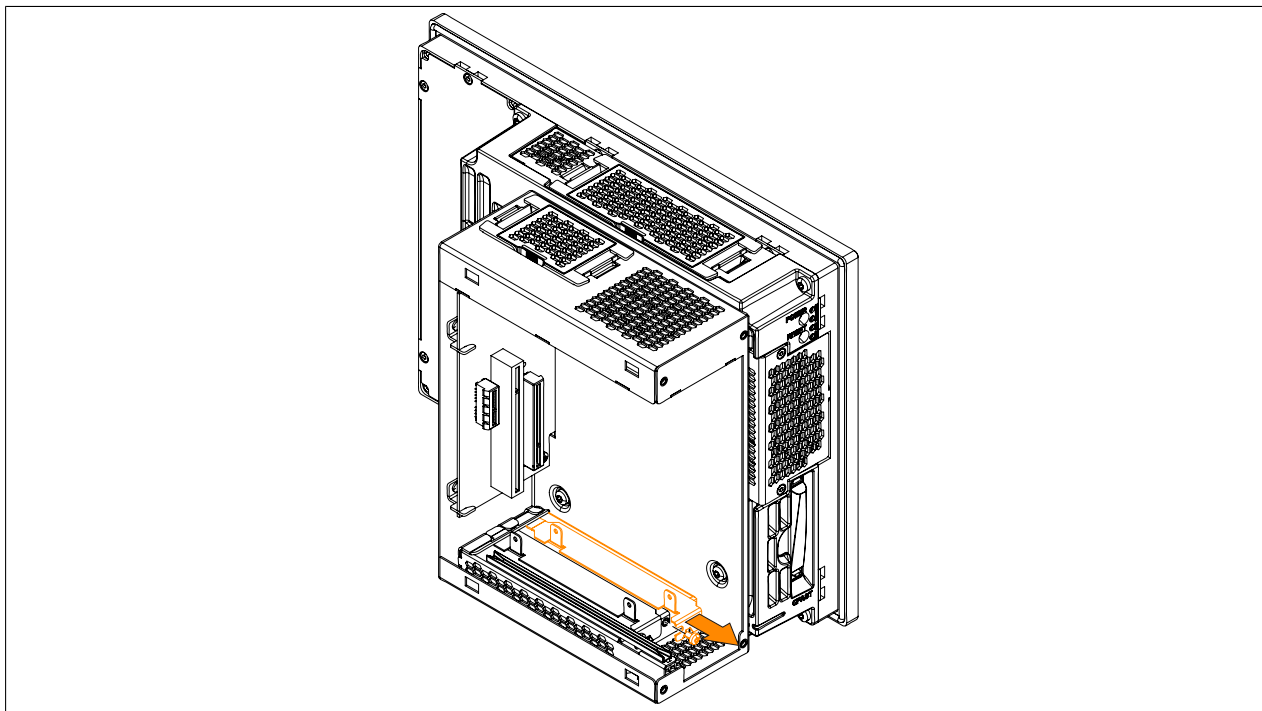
Torxschrauben lösen und Blindabdeckung entfernen
